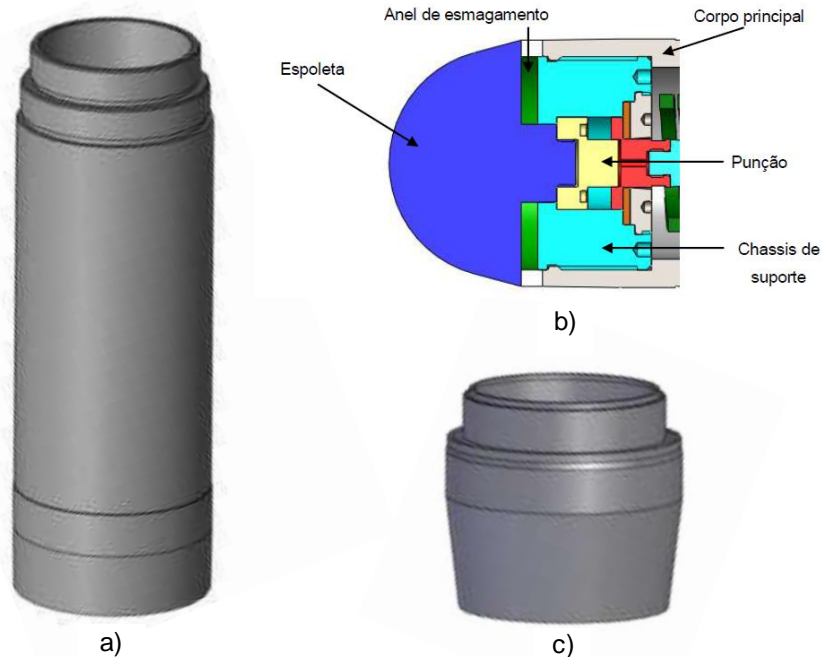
Elementos do chassis do FIREND<sup>®</sup>; a) Corpo do chassis; b) Subsistema da espoleta; c) Acoplamento [2].
